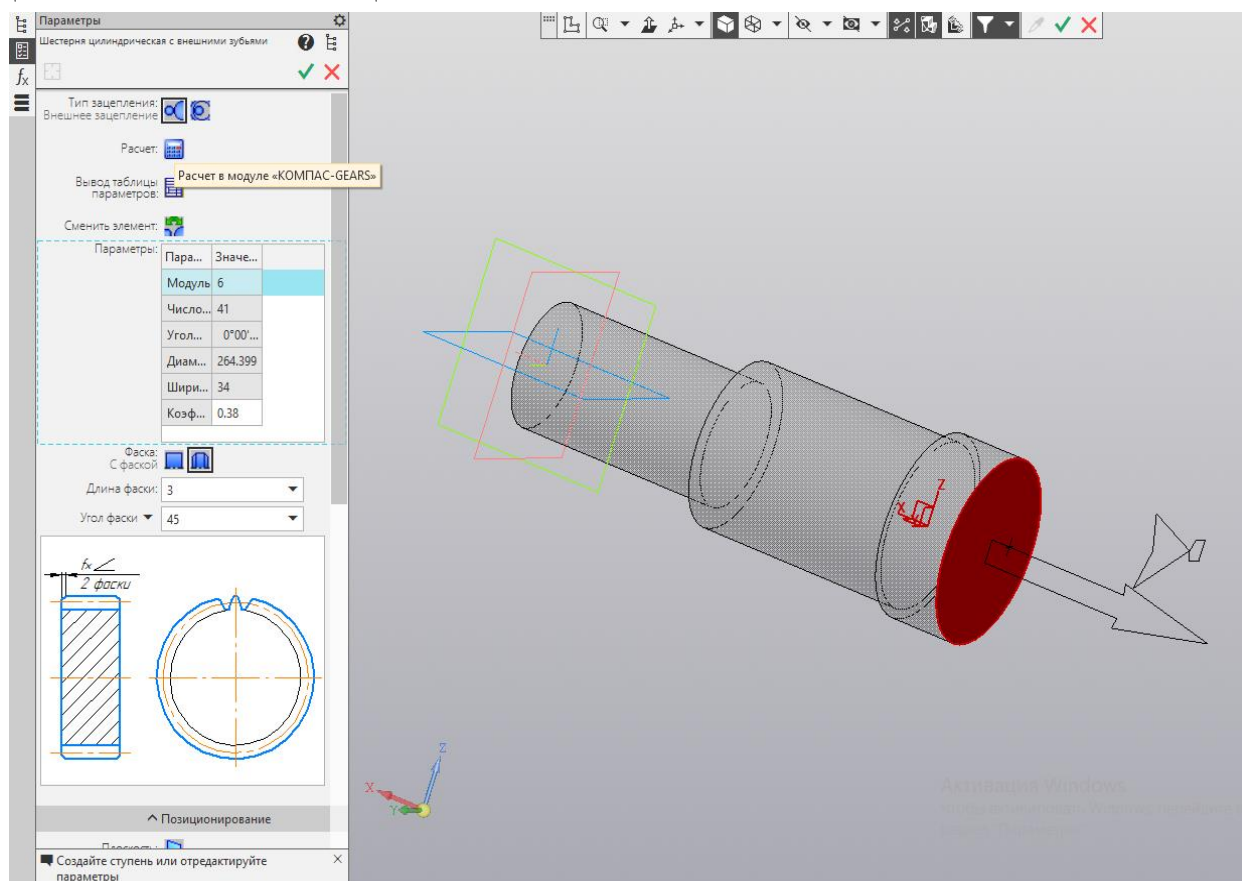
Выбор плоской грани для построения зубчатой ступени вала-шестерни
